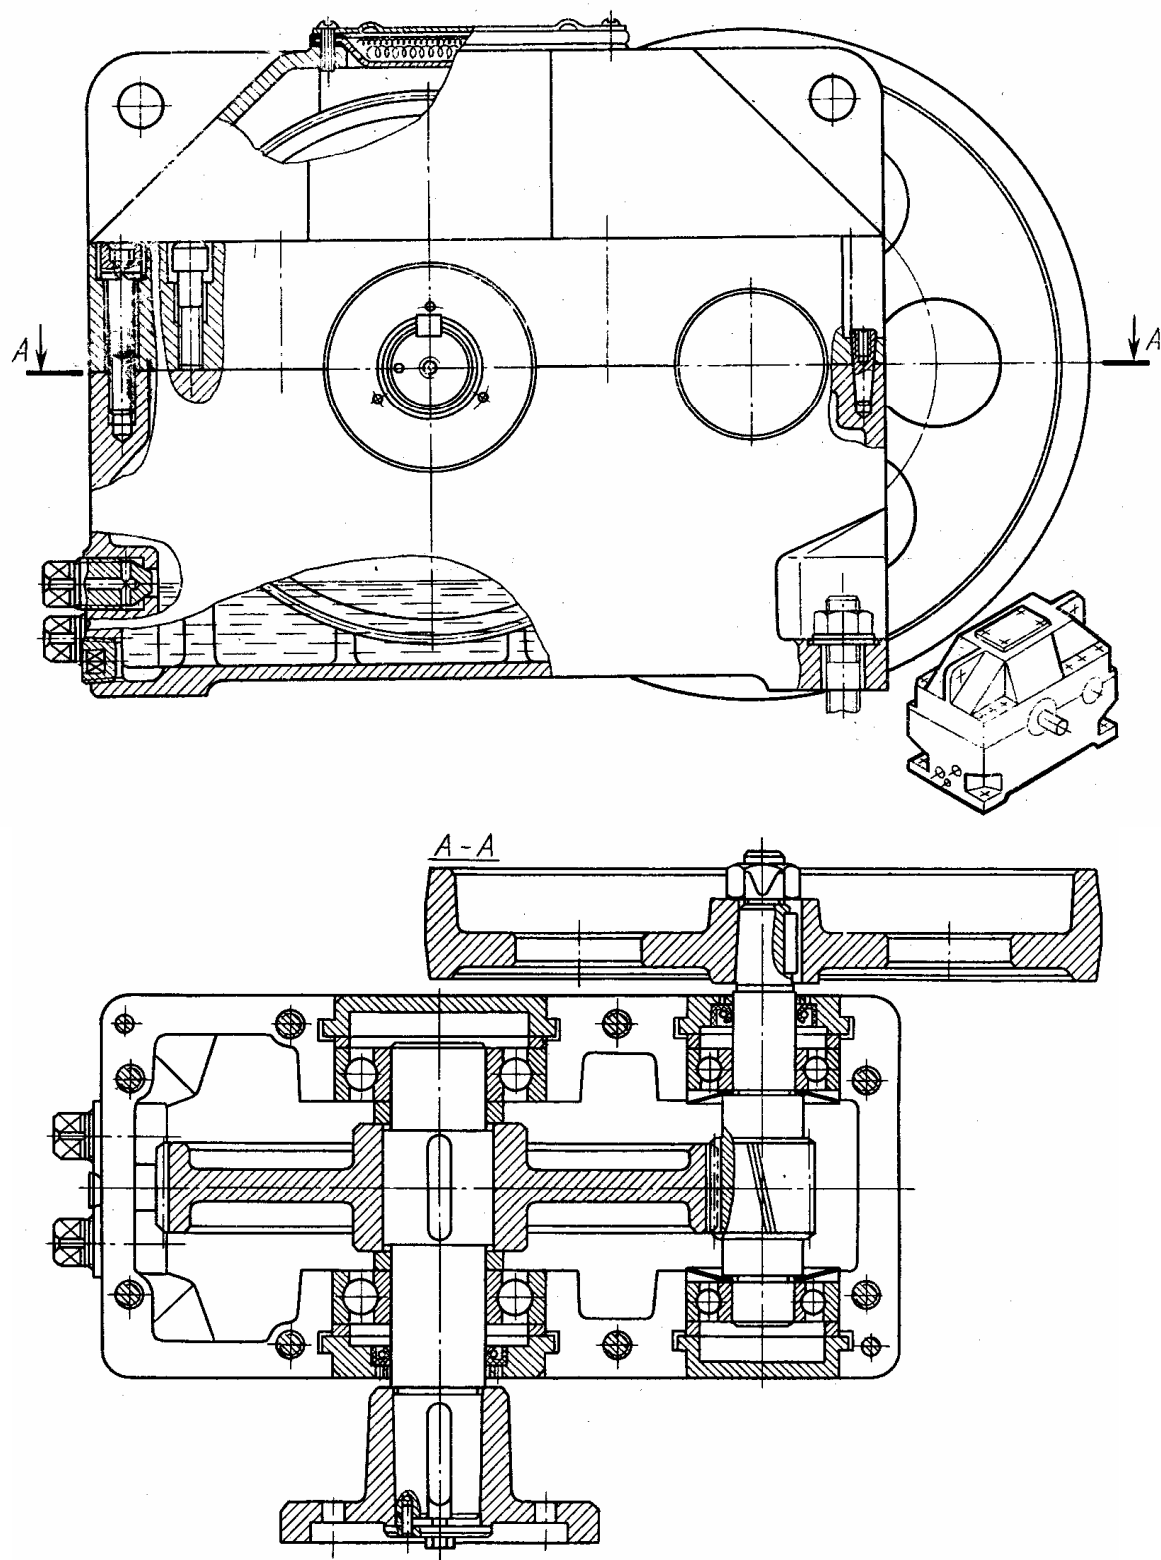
Редуктор (А9) цилиндрический одноступенчатый горизонтальный
